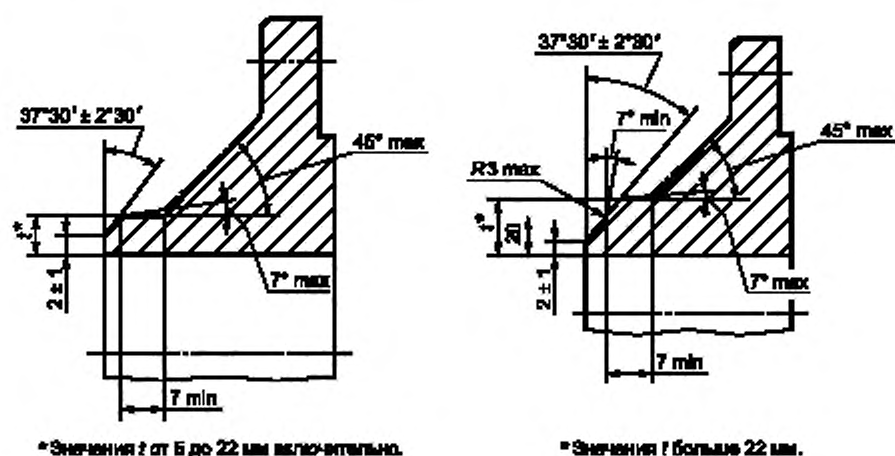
Разделка кромки под сварку для фланцев типа 11, ряд 2
